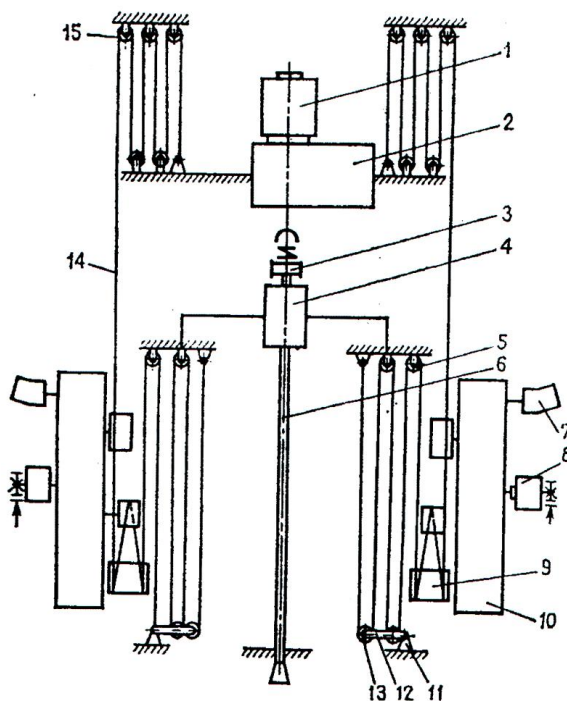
Кинематическая схема вращательно-подающего механизма станка СБШ–250/270–60, СБШ-320: 1 – электродвигатель; 2 – редуктор; 3 – шинно-шлицевая муфта; 4 – опорный узел; 5 – блоки натяжных устройств; 6 – штанга; 7 – гидромотор; 8 – электродвигатель; 9 – приводной барабан; 10 – лебедка; 11 – натяжное устройство; 12 – рычаг; 13 – блоки натяжных устройств; 14 – канат; 15 – верхние блоки
